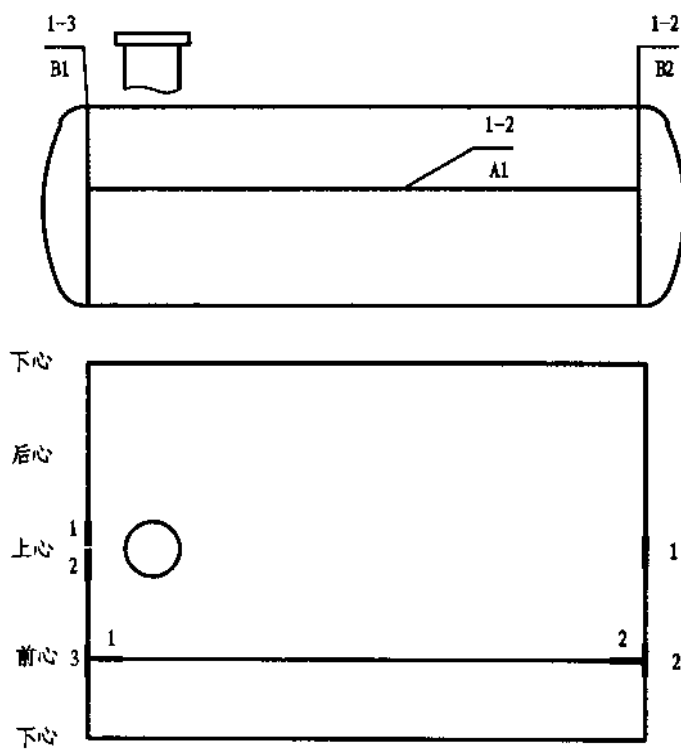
焊缝局部检测部位图 (主视图加展开图)
